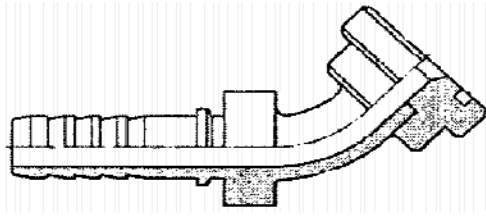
Terminale a 45° per collegamento a flangia SAE
